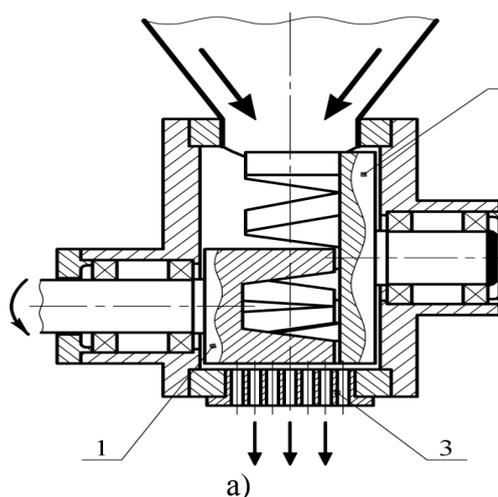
Универсальный измельчитель торцевого зацепления ИТЗ-01:
